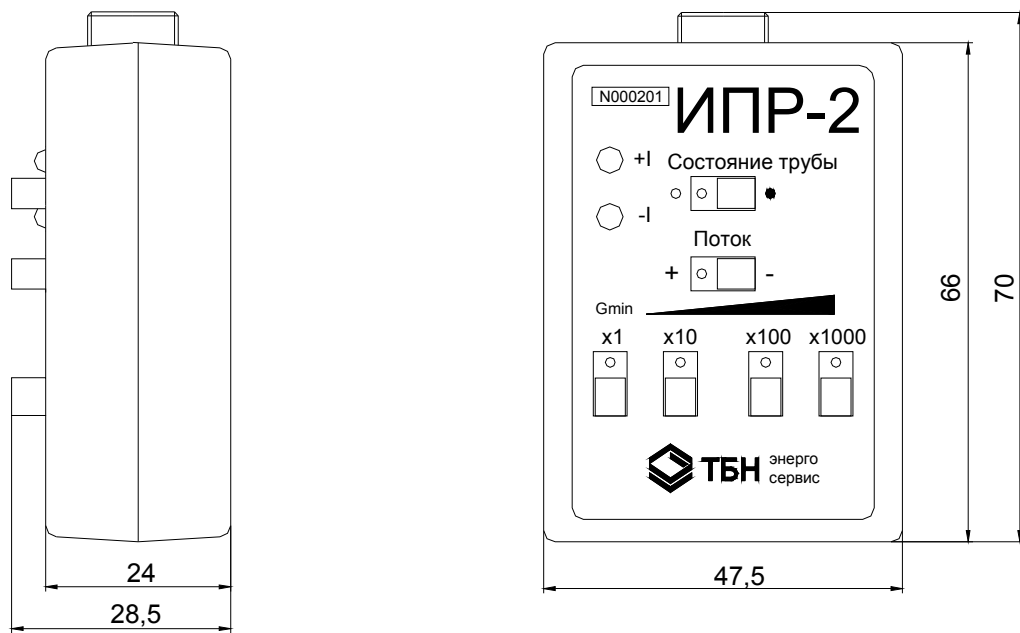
Габаритный чертеж имитатора преобразователя расхода
